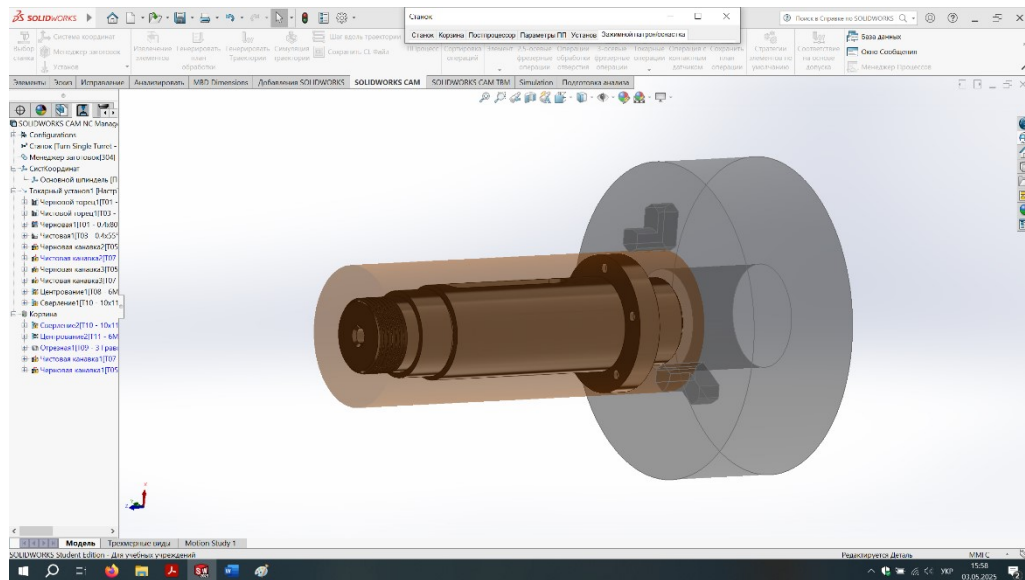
3D вигляд встановлення заготовки в патрон
